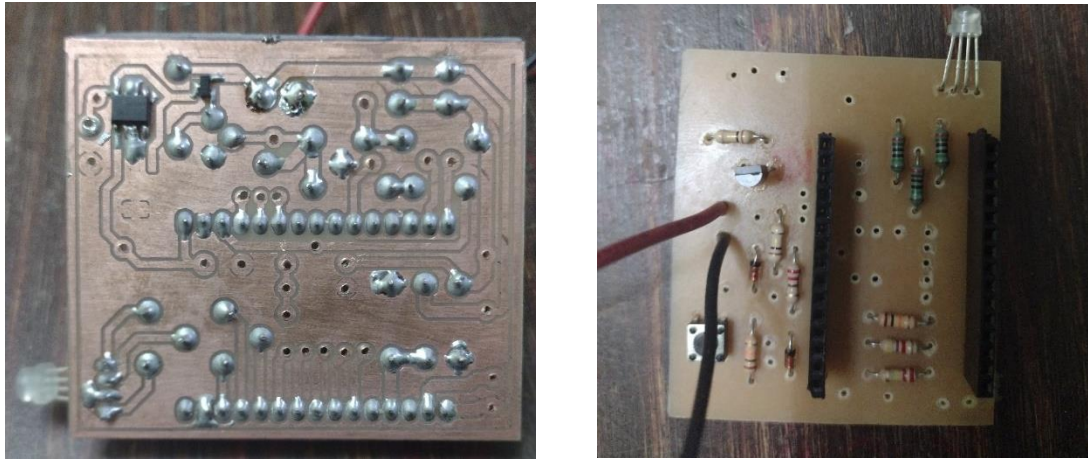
c: Diseño PCB finalizado – Versión Final.
